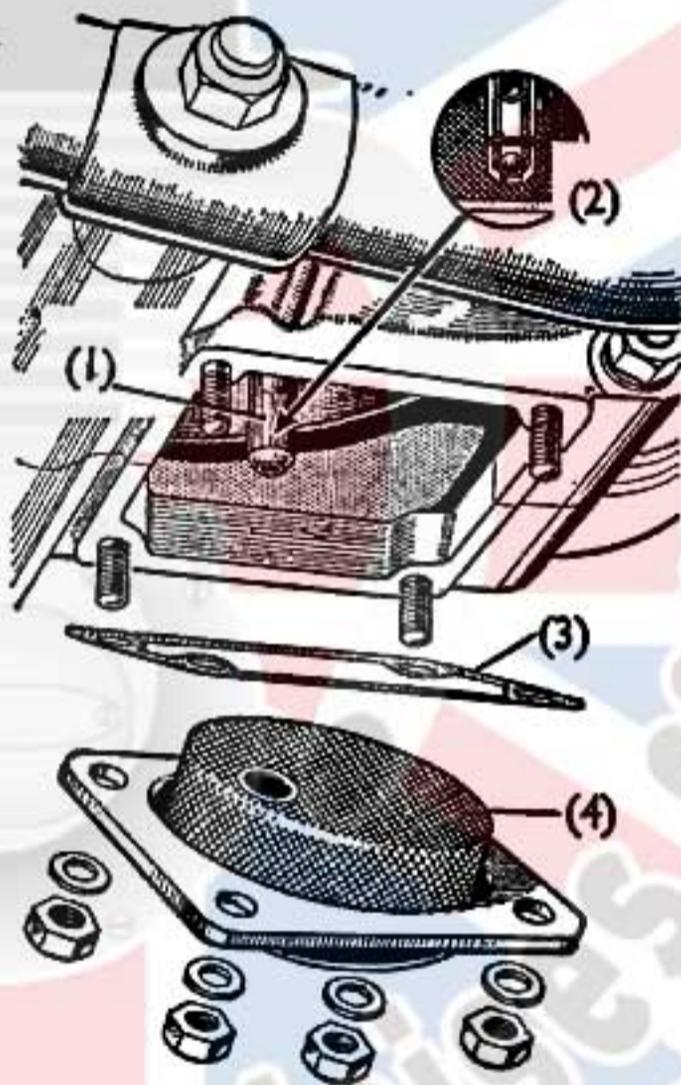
Filtre de carter et soupape à bille de la pompe.
